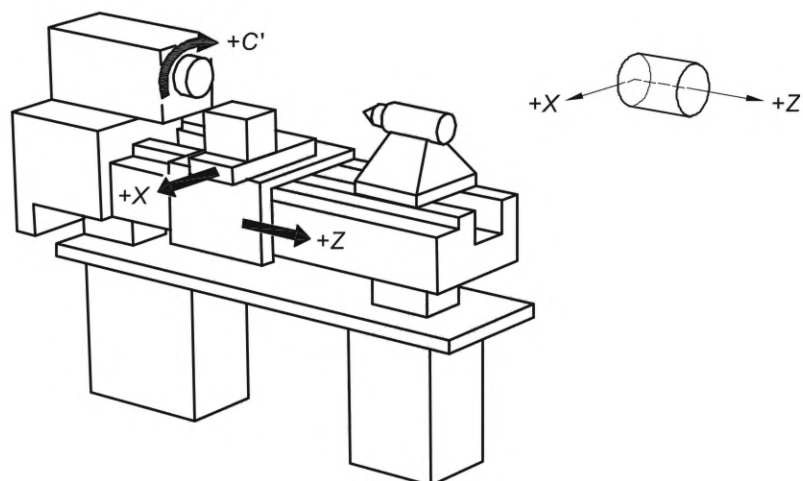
Токарно-винторезный станок с горизонтальными направляющими суппорта
